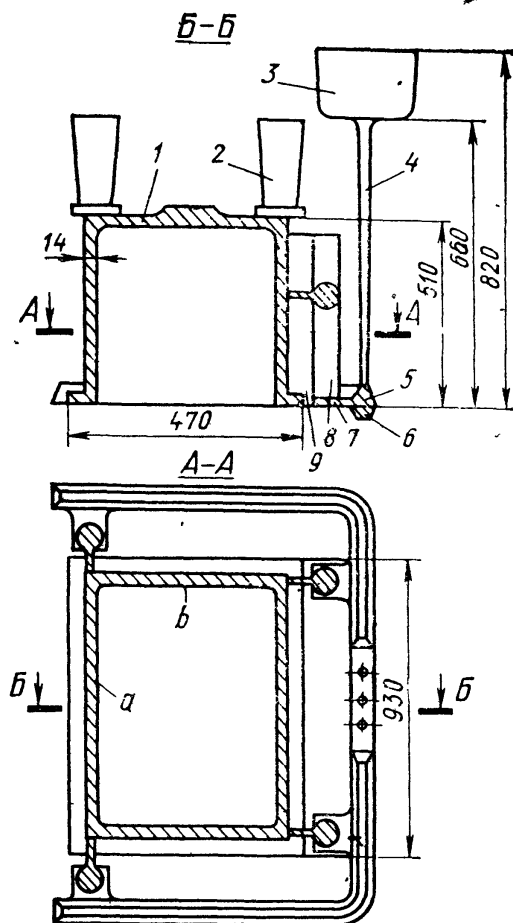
Схема устройства вертикально-щелевой литниковой системы для отливки корпуса:
